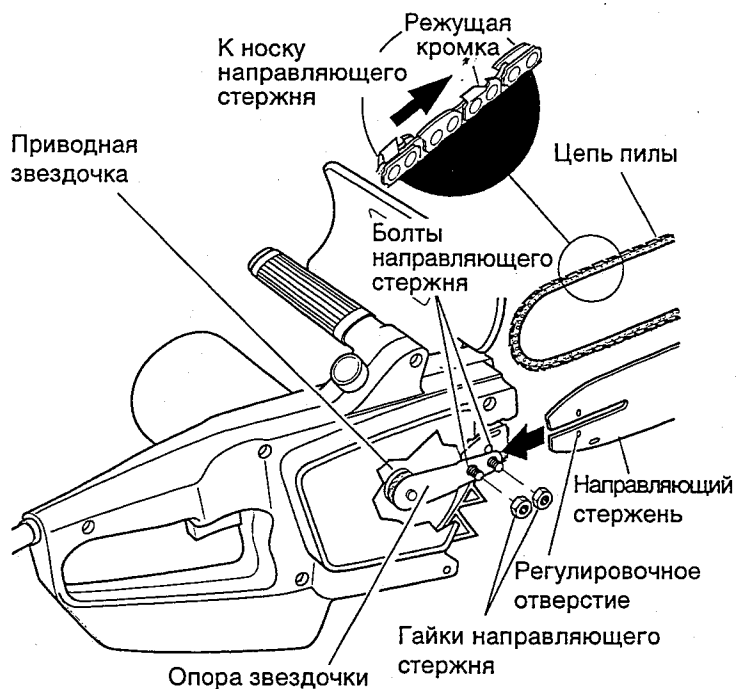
Сборка направляющего стержня, цепи и ограждения для руки
